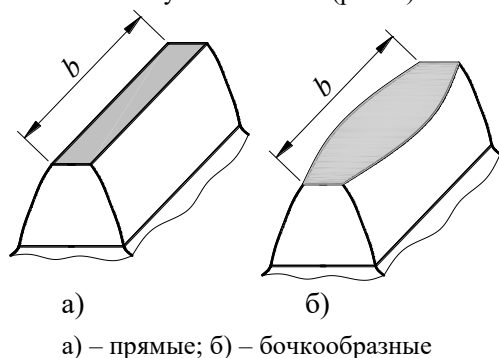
Эвольвентные зубья с образующими боковых поверхностей
